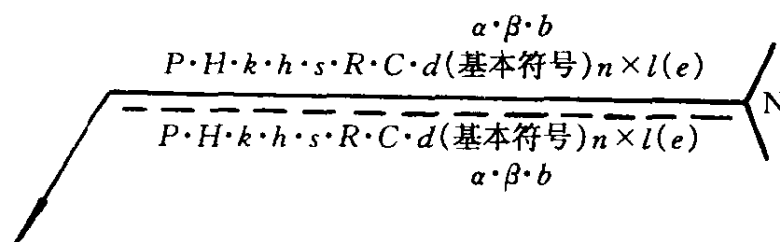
焊缝尺寸符号及数据的标注原则
